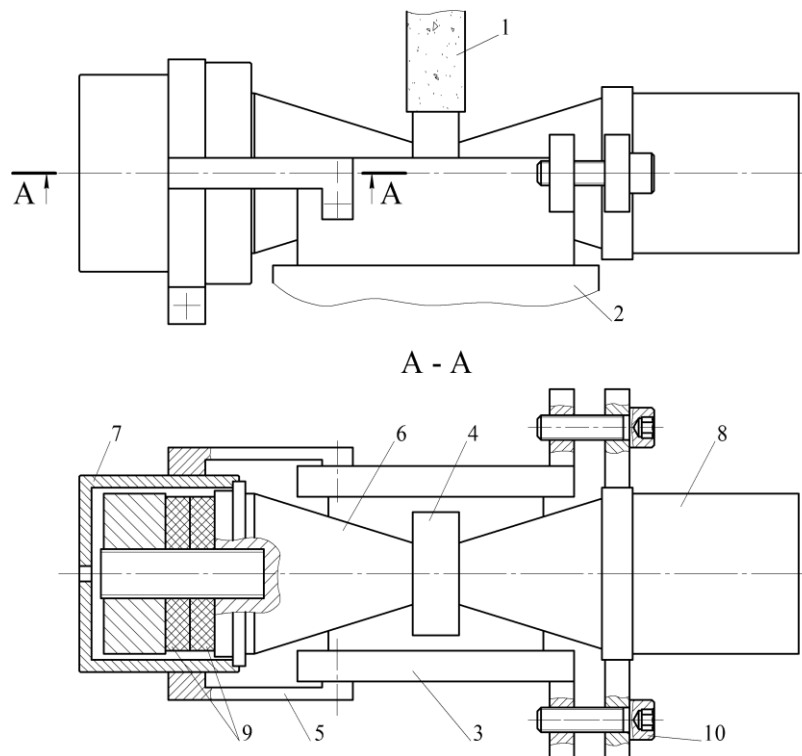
Схема наложения УЗК на заготовку: 1 — шлифовальный круг; 2 — магнитная плита станка; 3 — рамка; 4 — заготовка; 5 — кронштейн; 6 — излучатель; 7 — корпус; 8 — опора; 9 — пьезопреобразователи; 10 — винты
